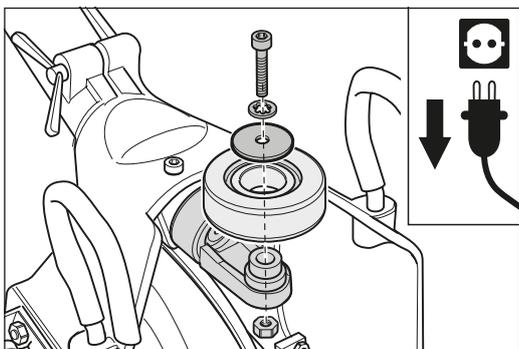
Vuelque la máquina hacia adelante mediante el estribo portante. Extraiga el tornillo junto con las arandelas y las tuercas del centro de la rueda y desmonte la rueda trasera. El ensamble se realiza por el orden inverso. ¡Asegúrese de que la máquina esté muy estable!
